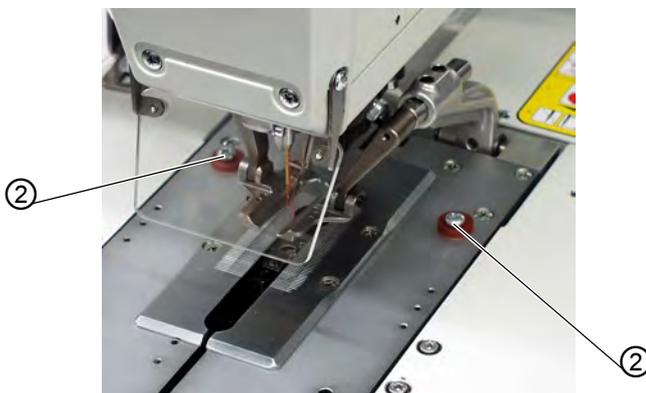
Remover os dispositivos de fixação utilizados no transporte da parte superior da máquina
